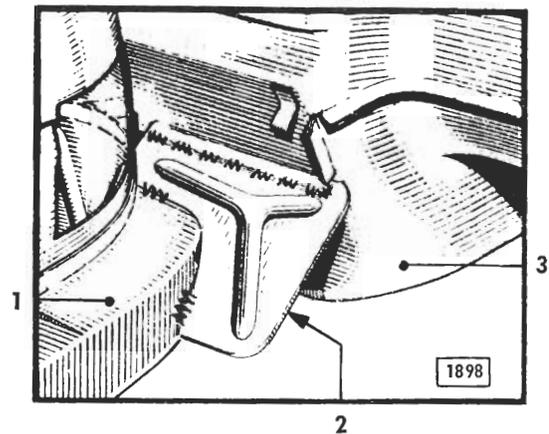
Auf rechter Wagenseite Abschirmblech an Längsträger und Stirnwandflansch lichtbogengeschweißt
